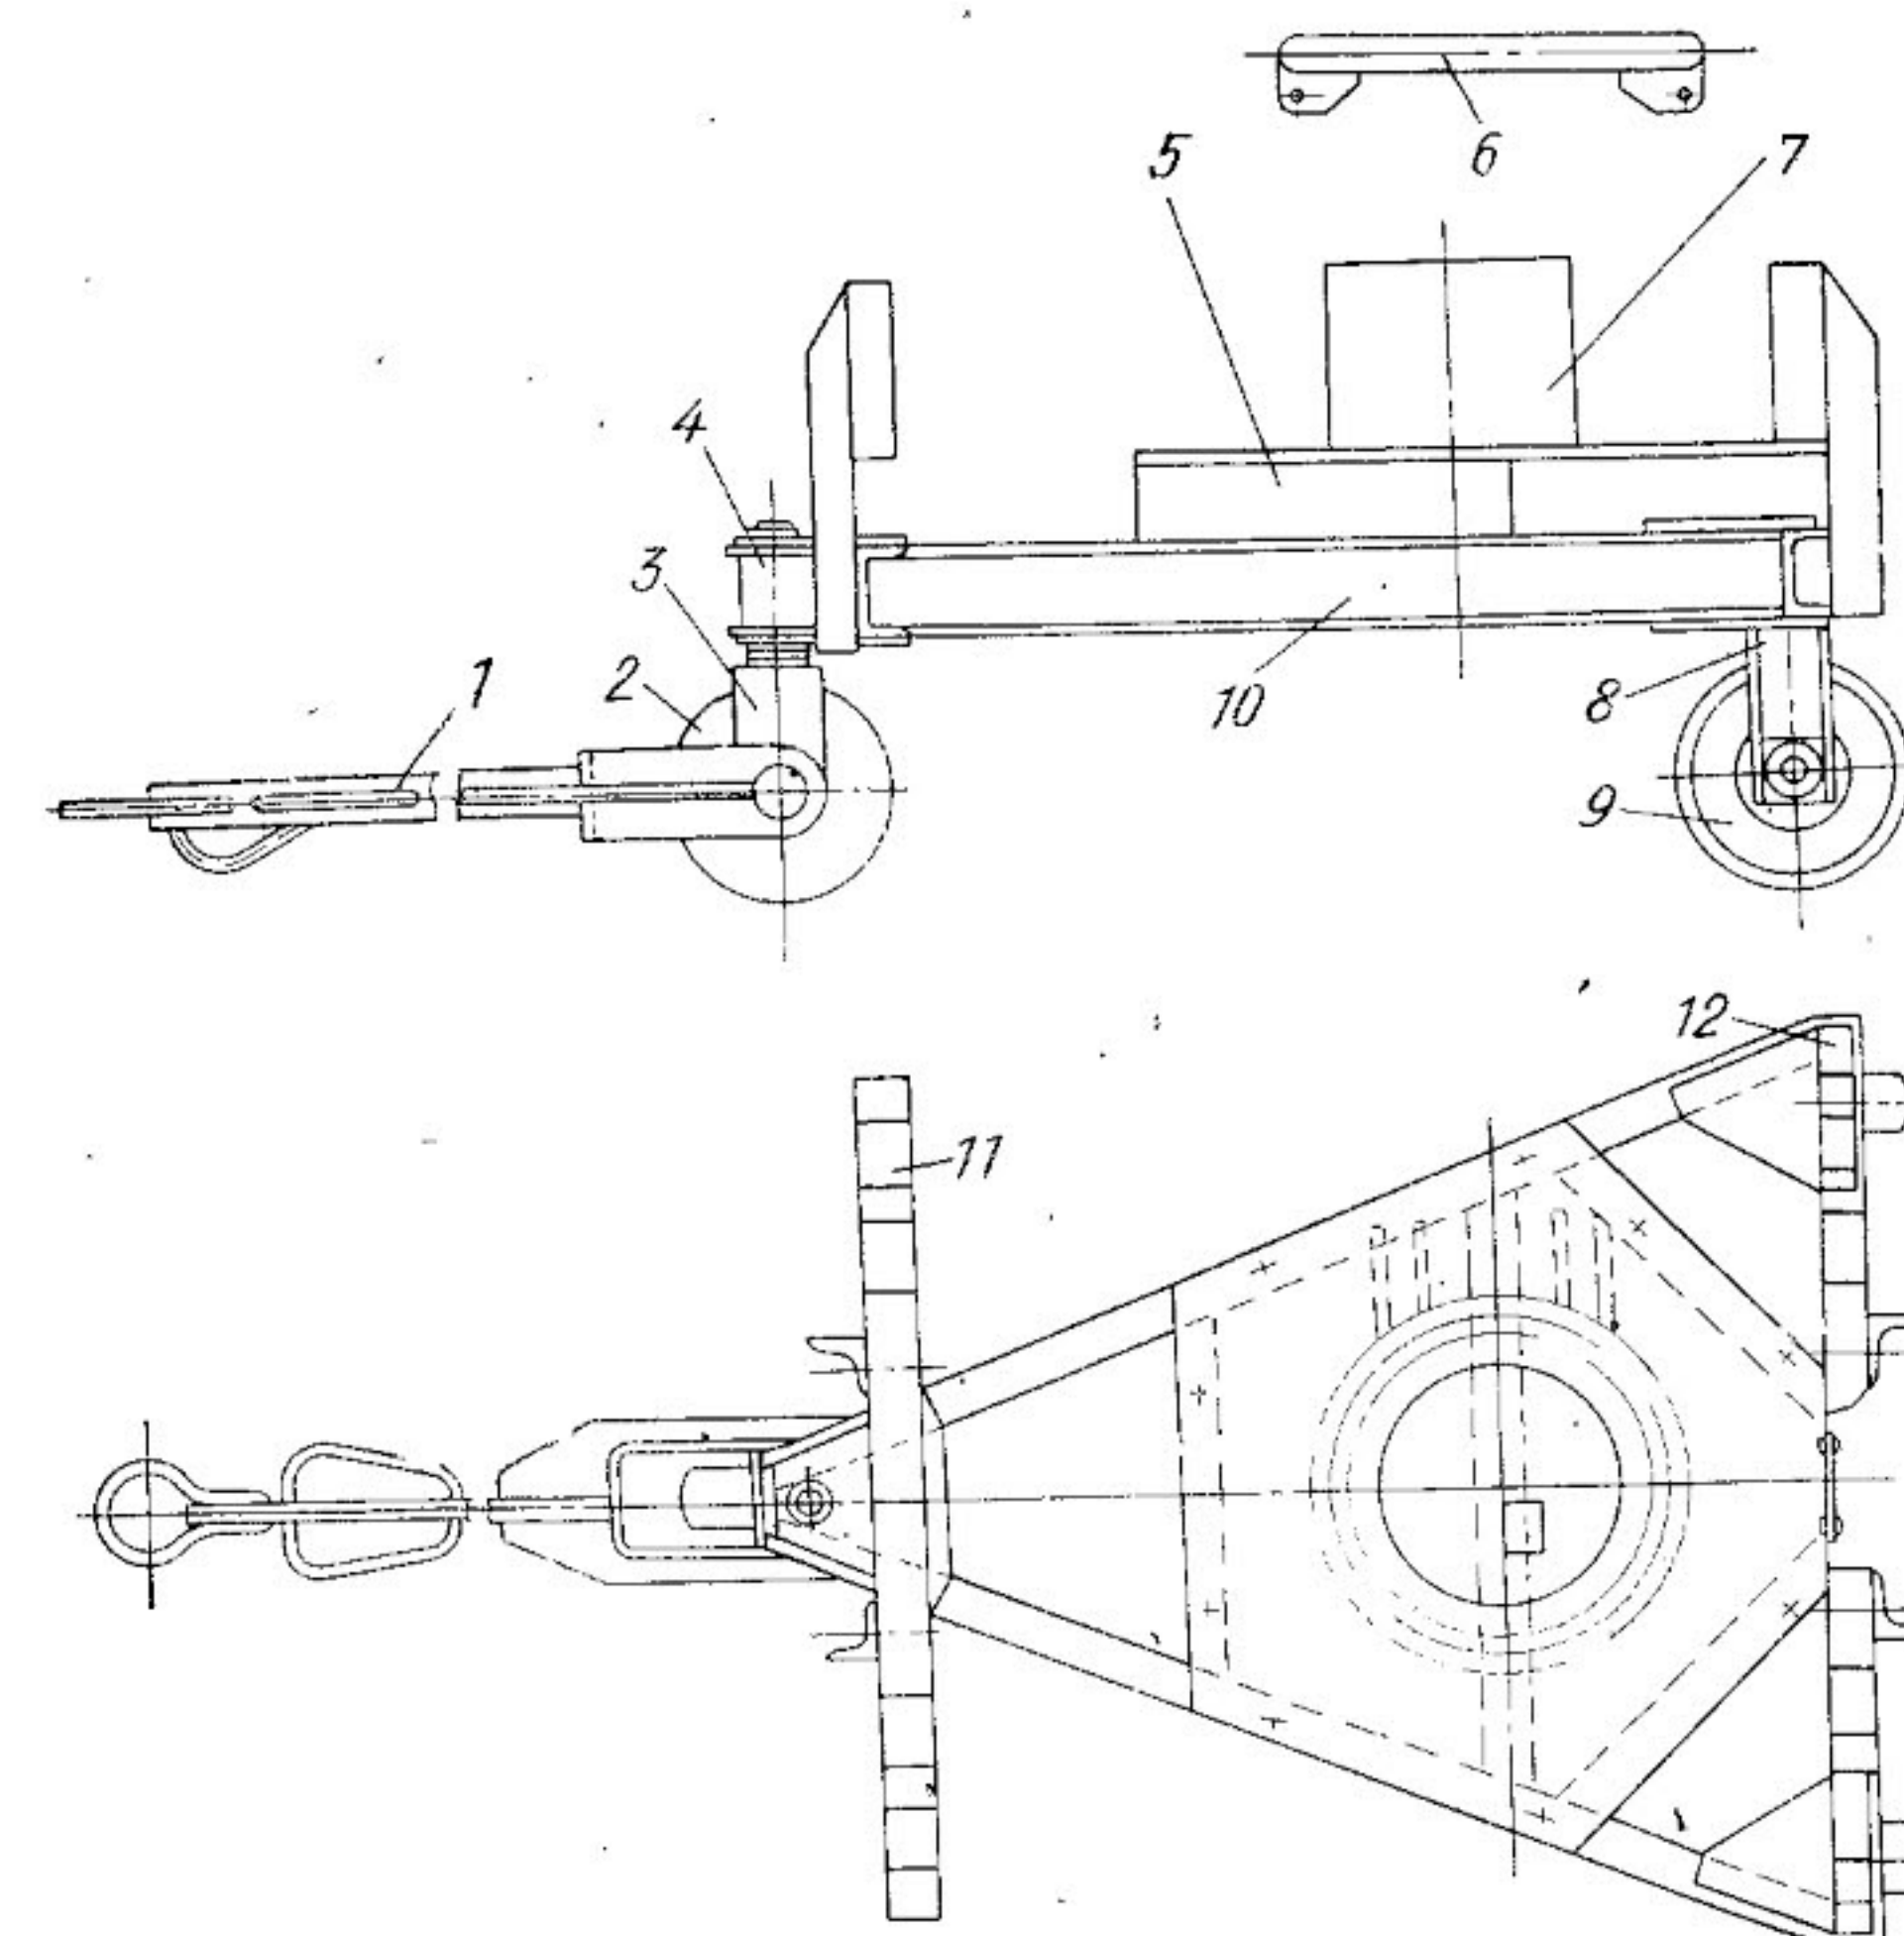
Тележка для транспортировки втулки несущего винта, или автомата перекоса, или лопастей хвостового винта:
